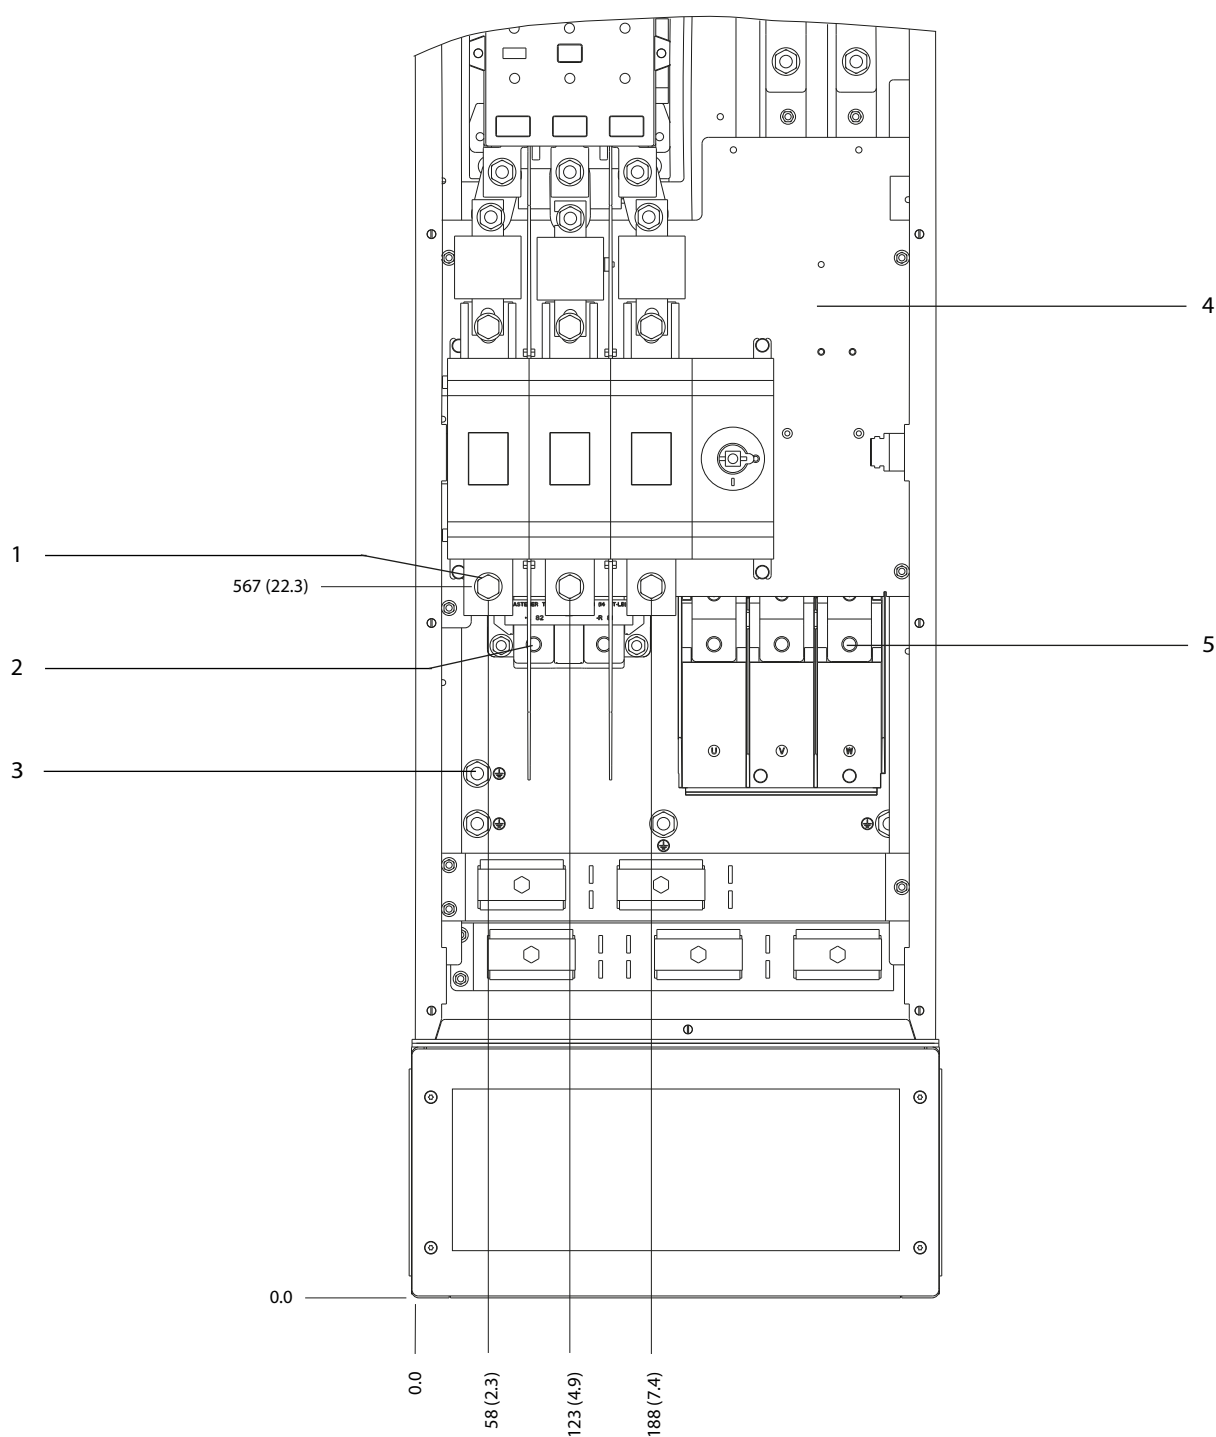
Dimensões do terminal do D8h com opcional de contator (vista frontal)
